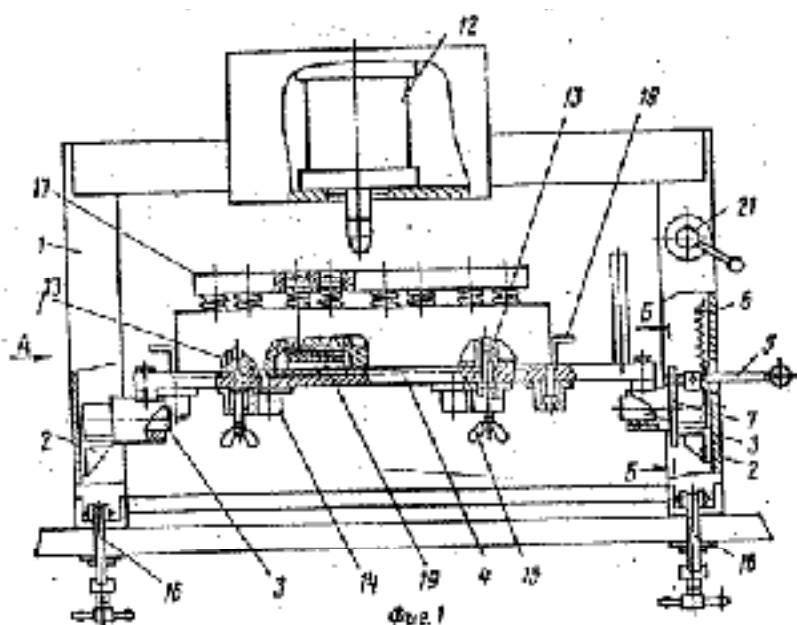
Стенд для разборки и сборки блоков цилиндров двигателей
